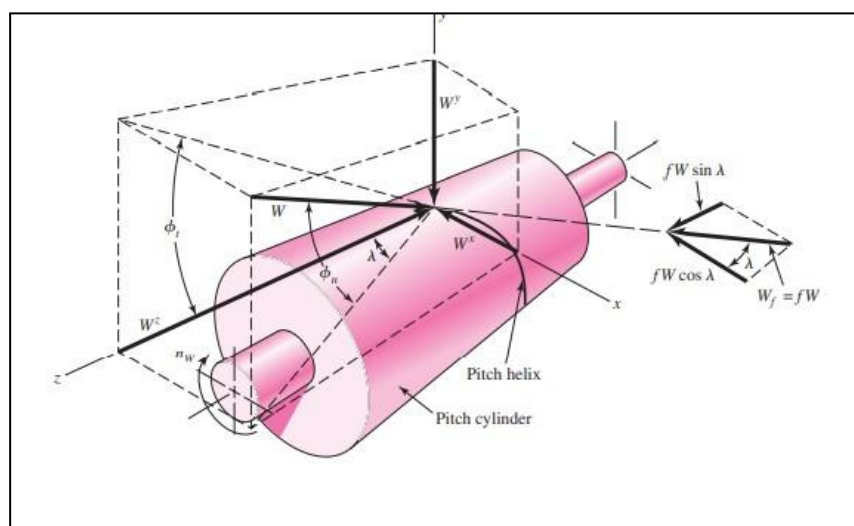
Fuerzas que aparecen en el sistema de transmisión Engranaje -Tornillo sin fin. [45]
